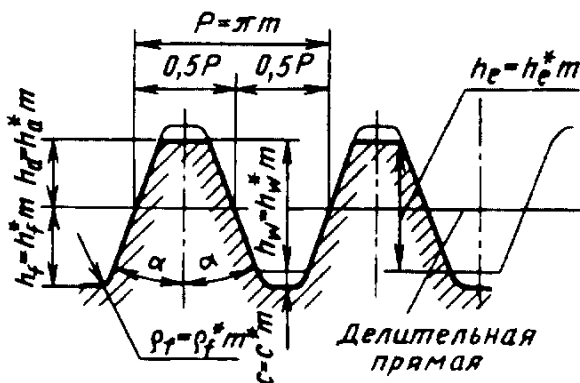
Исходный контур зубчатых цилиндрических колес эвольвентного зацепления по ГОСТ 13755—81 и конических колес с прямыми зубьями по ГОСТ 13754—81
